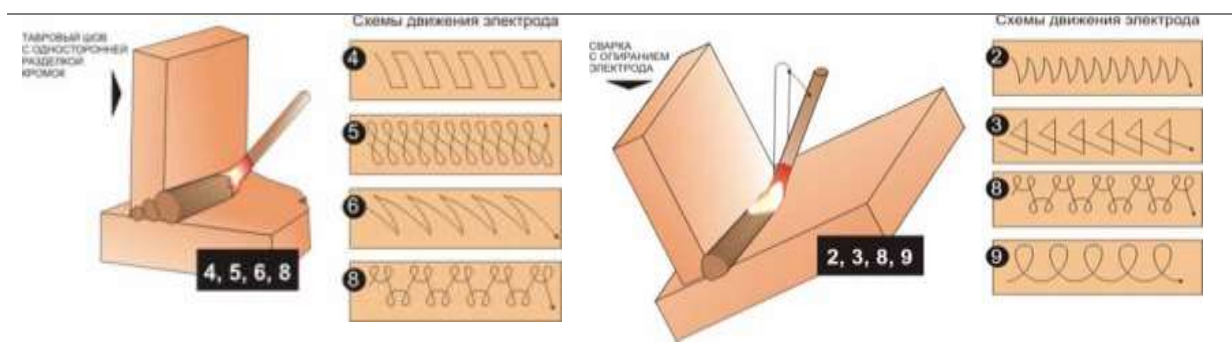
Схемы движения электрода при сварке угловых соединений
